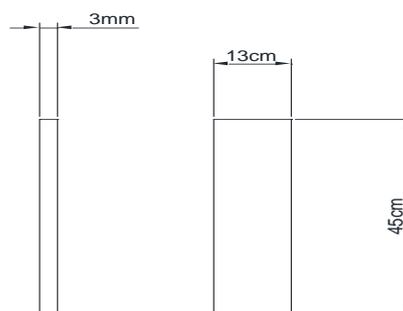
Desenho do dimensionamento a partir do AutoCAD
